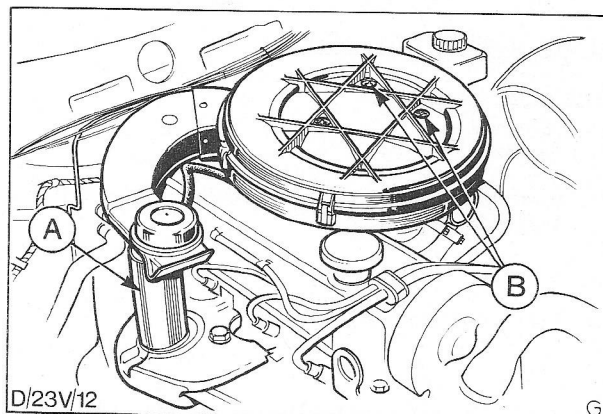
Luchtfilter (OHC-motor afgebeeld).
